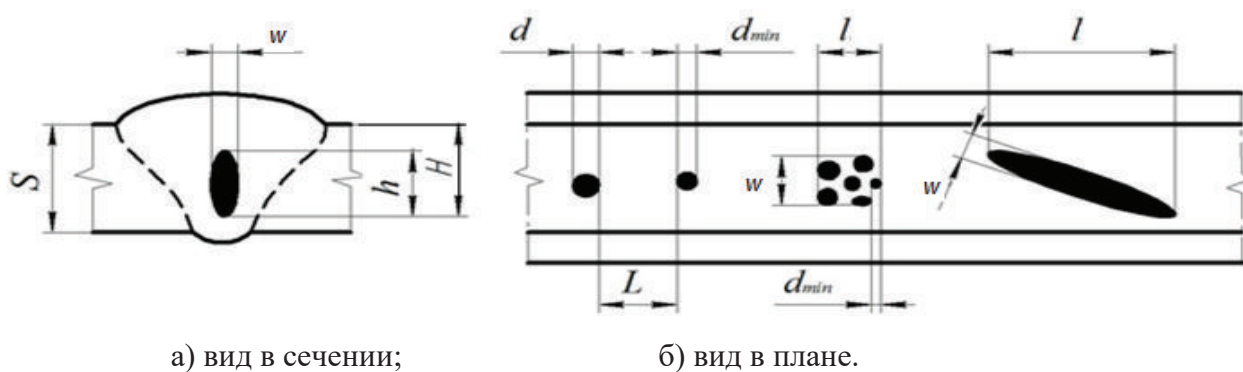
Схематическое изображение сварного соединения и определение размеров дефектов
